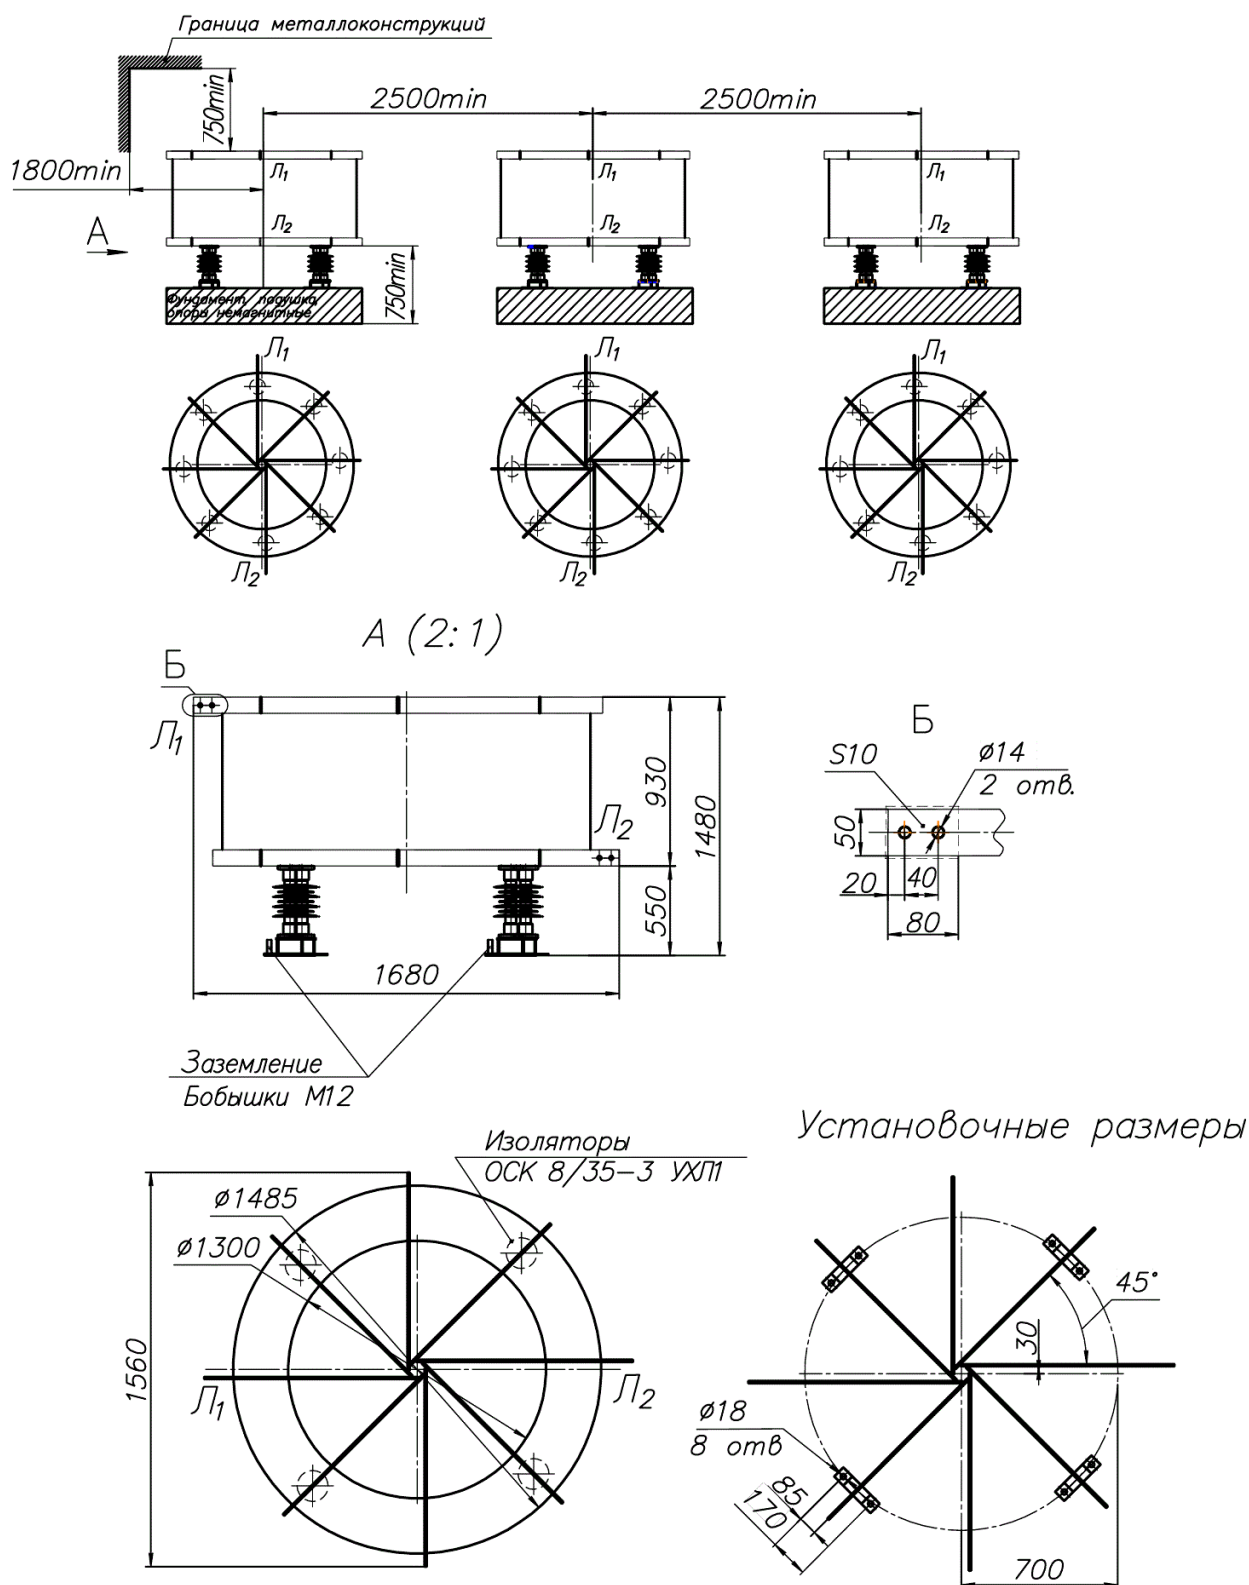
Габаритный чертеж реактора 8,45 мГн, 464 А
